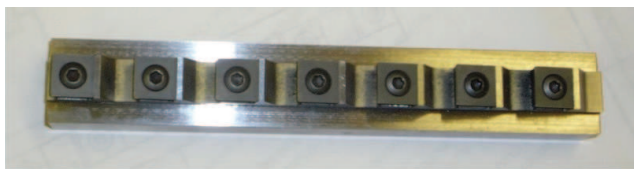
Общий вид сборной протяжки с СМП для обработки замка лопатки
